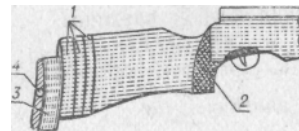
Регулировка положения затыльника пневматической винтовки «312» (ГДР)
